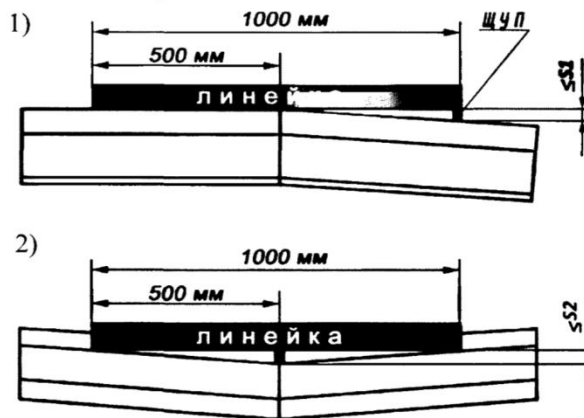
Схема измерения прямолинейности наплавленного сварного стыка:
